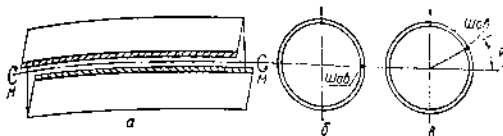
Скручивание тонкостенной цилиндрической оболочки при сварке продольного шва
